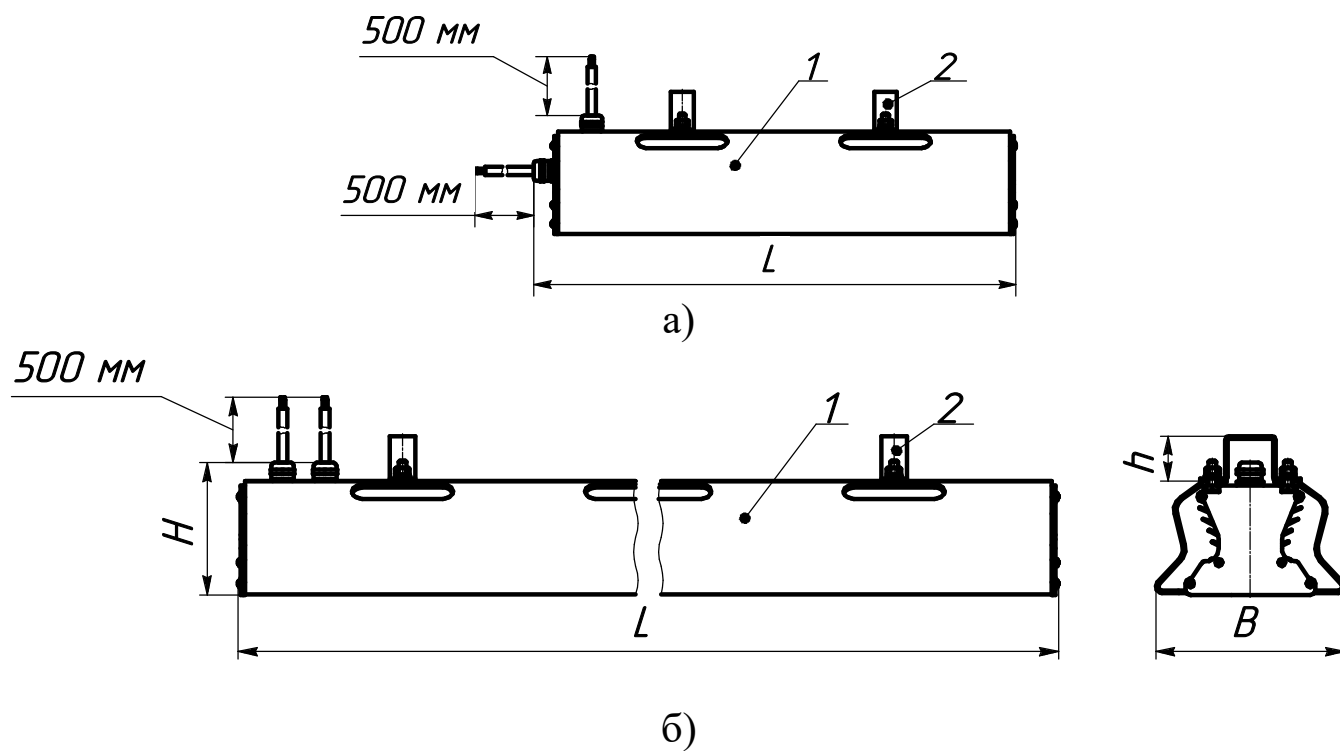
Внешний вид и габаритные размеры светильников с
